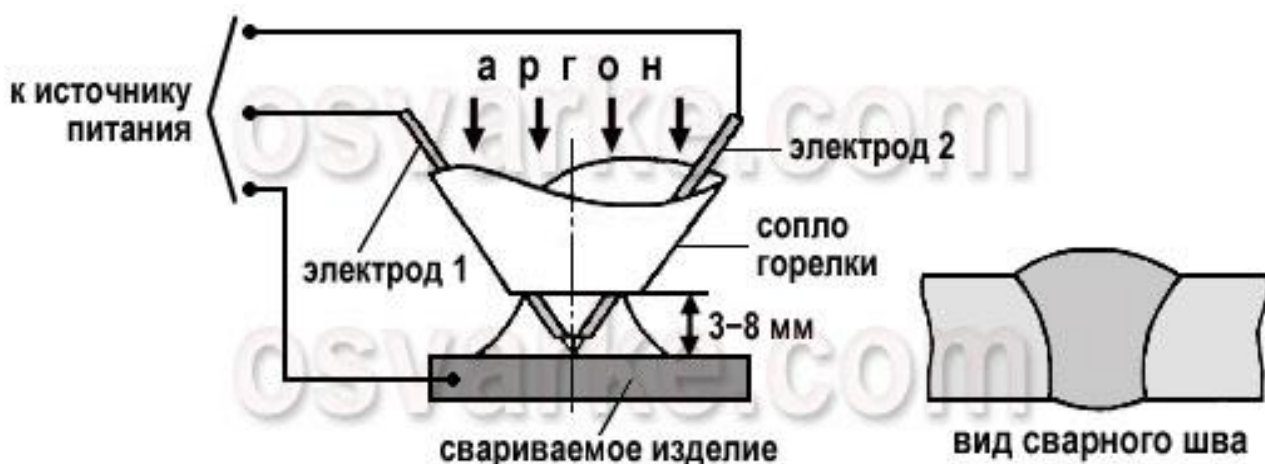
Схема выполнения сварки трёхфазной дугой
